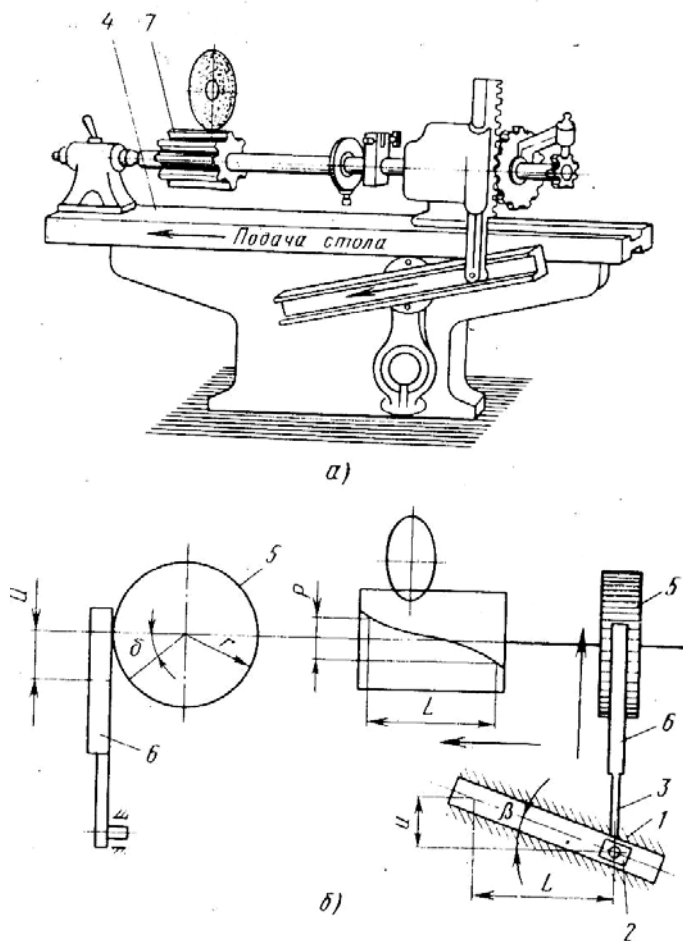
Схема устройства для заточки передней винтовой поверхности червячной модульной фрезы:
